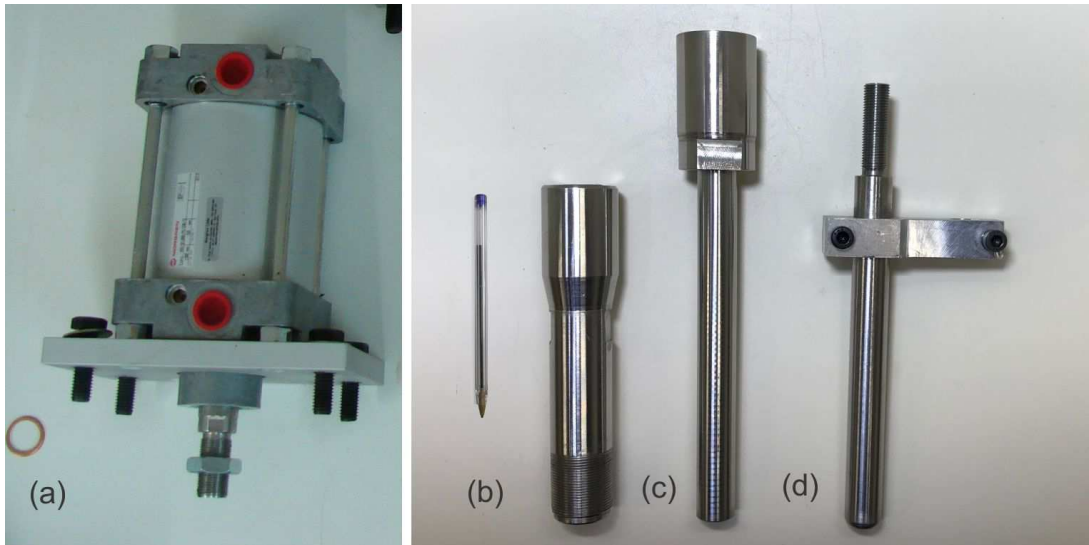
Cilindro pneumático e conexões para aplicação de carga vertical.
